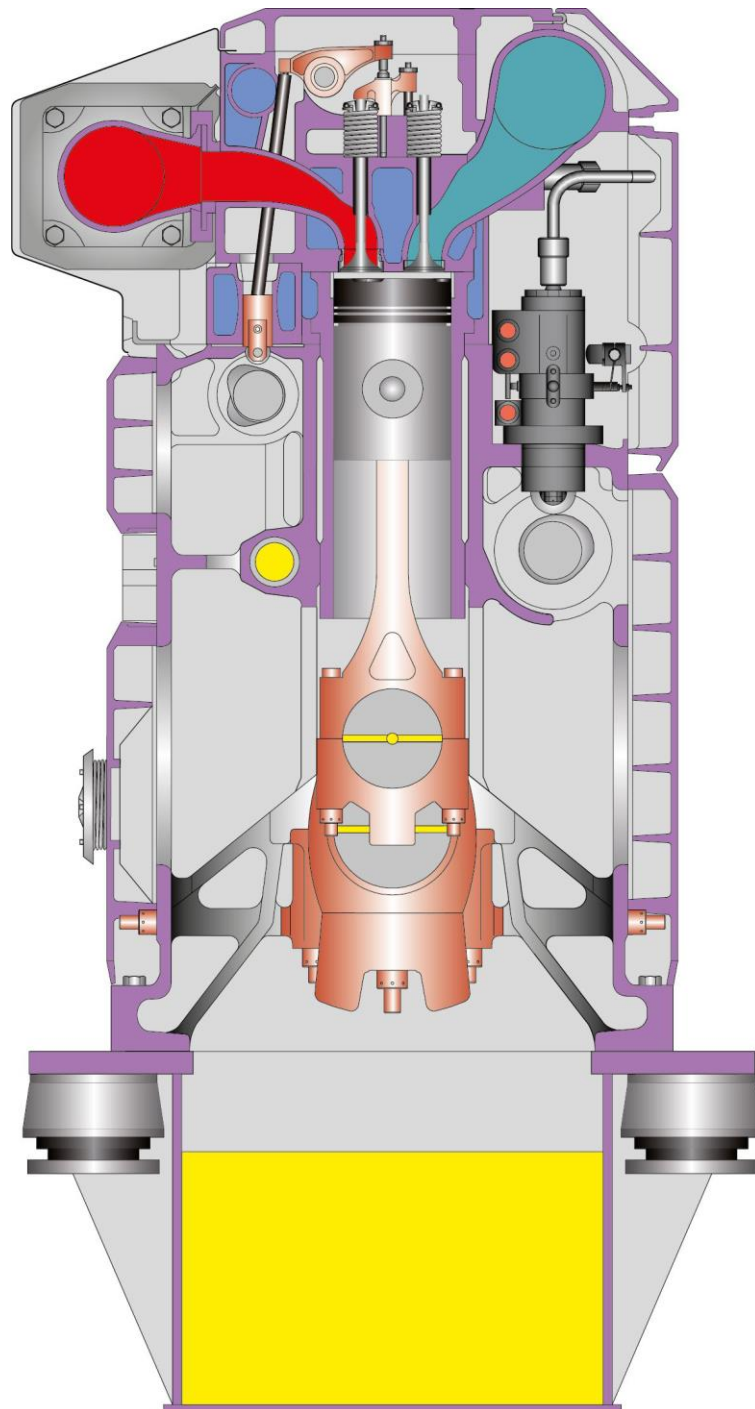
Поперечний переріз двигуна 8ЧН16/24
